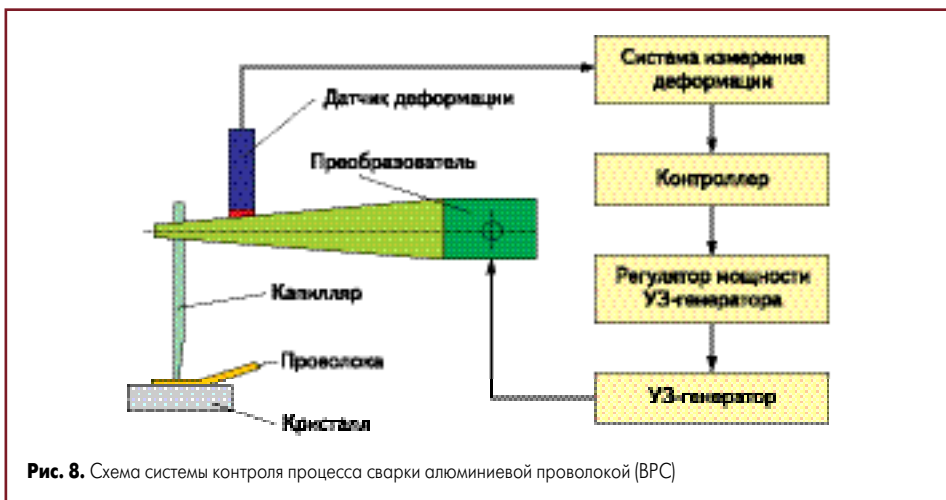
Схема системы контроля процесса сварки алюминиевой проволокой (BPC)
